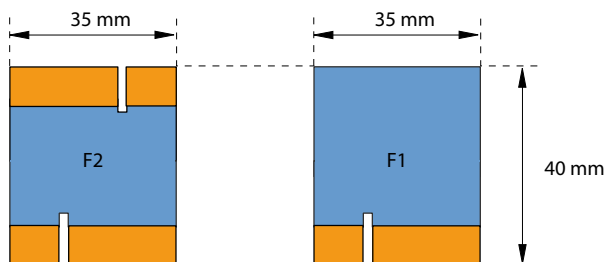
Dimensions de l'adaptateur de câblage (forme de construction F)
